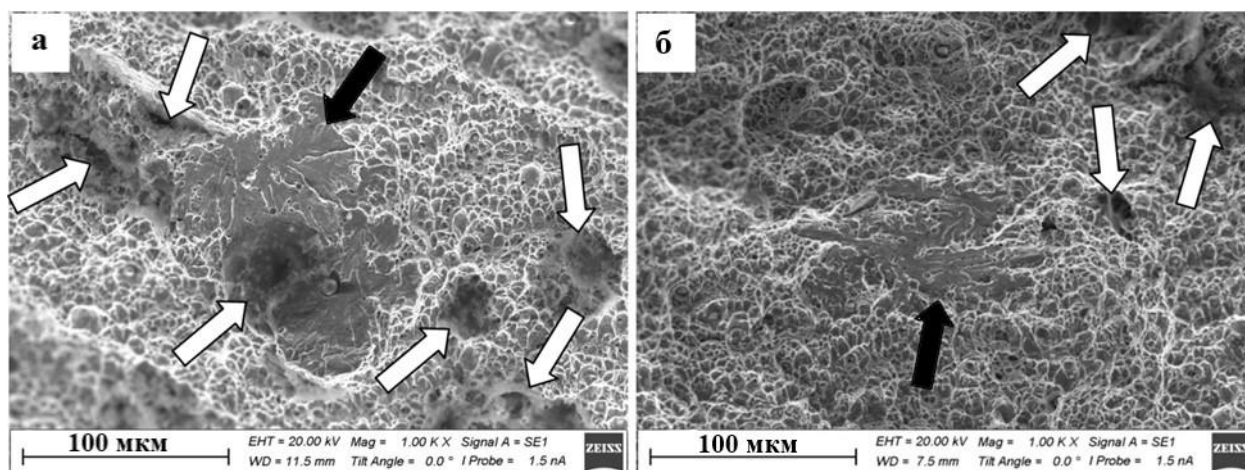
Электронно-микроскопическое изображение поверхности излома металла наплавов №1 (а) и №2 (б) (светлыми стрелками указаны микро- и макропоры, несплошности металла, стрелками черного цвета – участки квазихрупкого излома)
